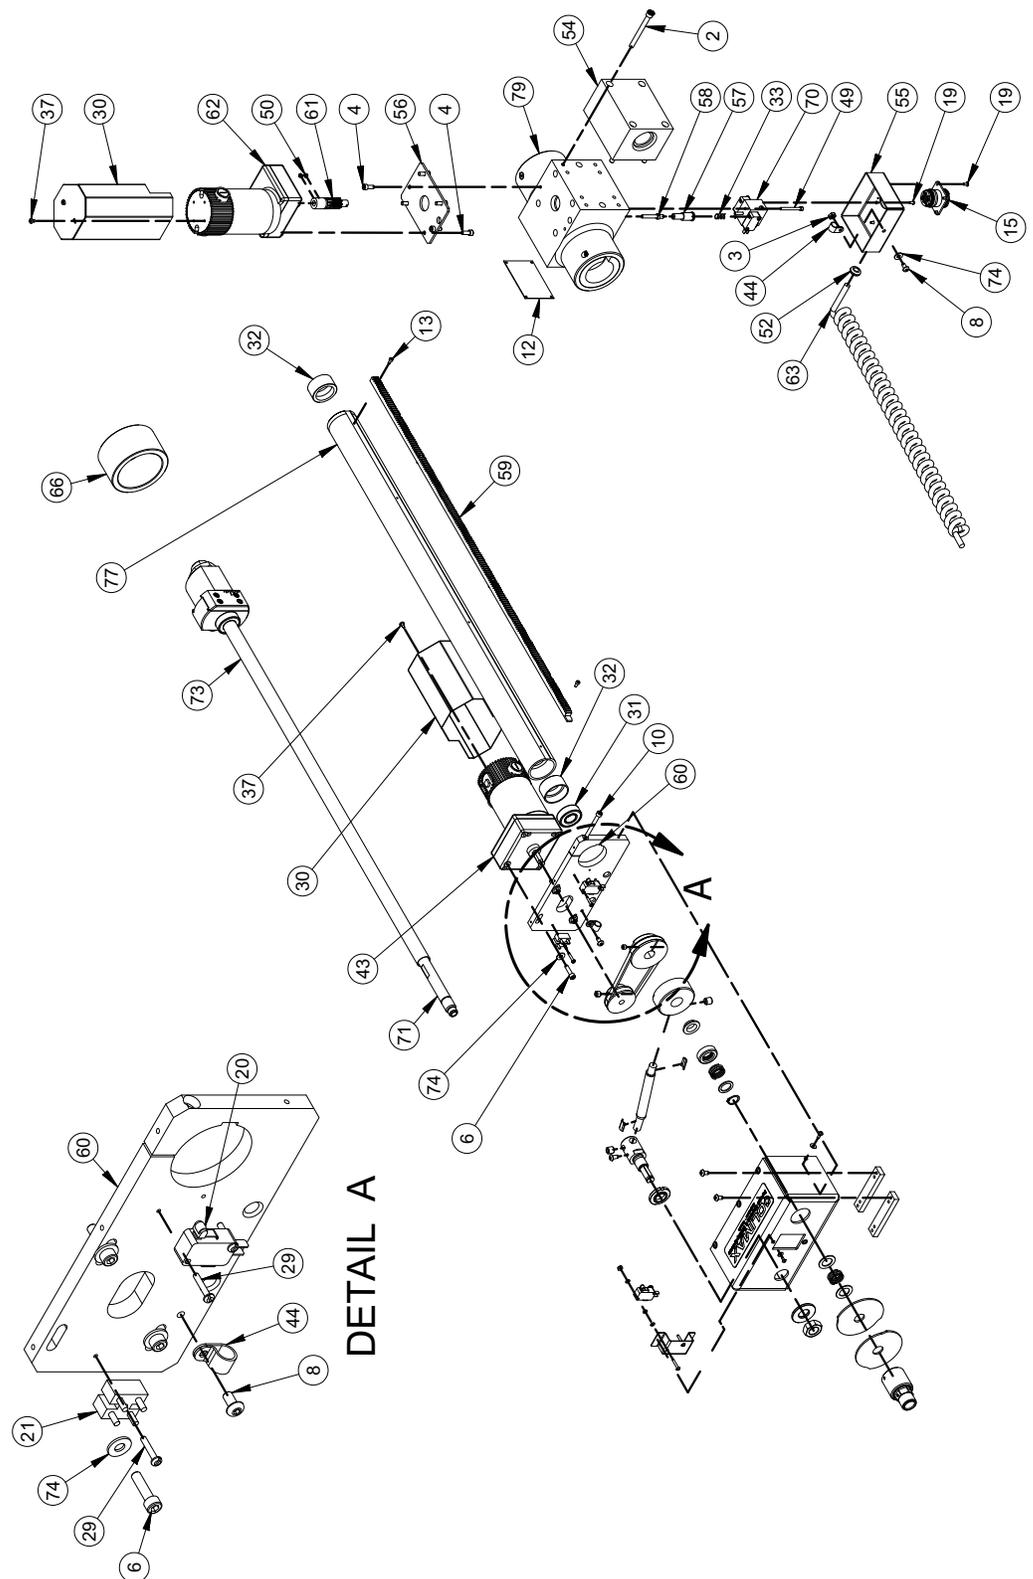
ENSEMBLE 1 DE TÊTE DE SOUDAGE (PRODUIT PERSONNALISÉ UNIQUEMENT) (RÉF. 91808)
